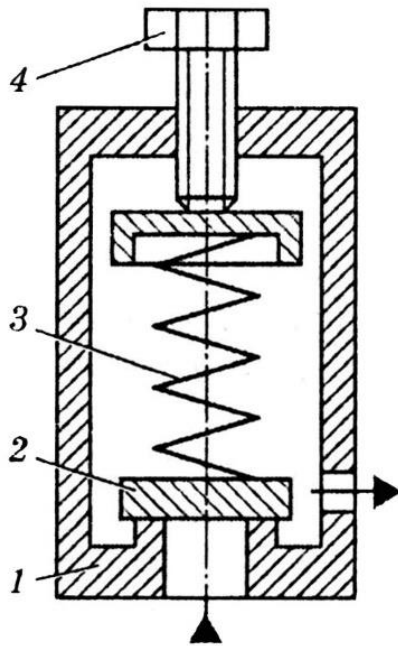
Схема запобіжного клапана прямої дії тарілчастого: 1 – корпус; 2 – тарілка; 3 – пружина; 4 – гвинт
